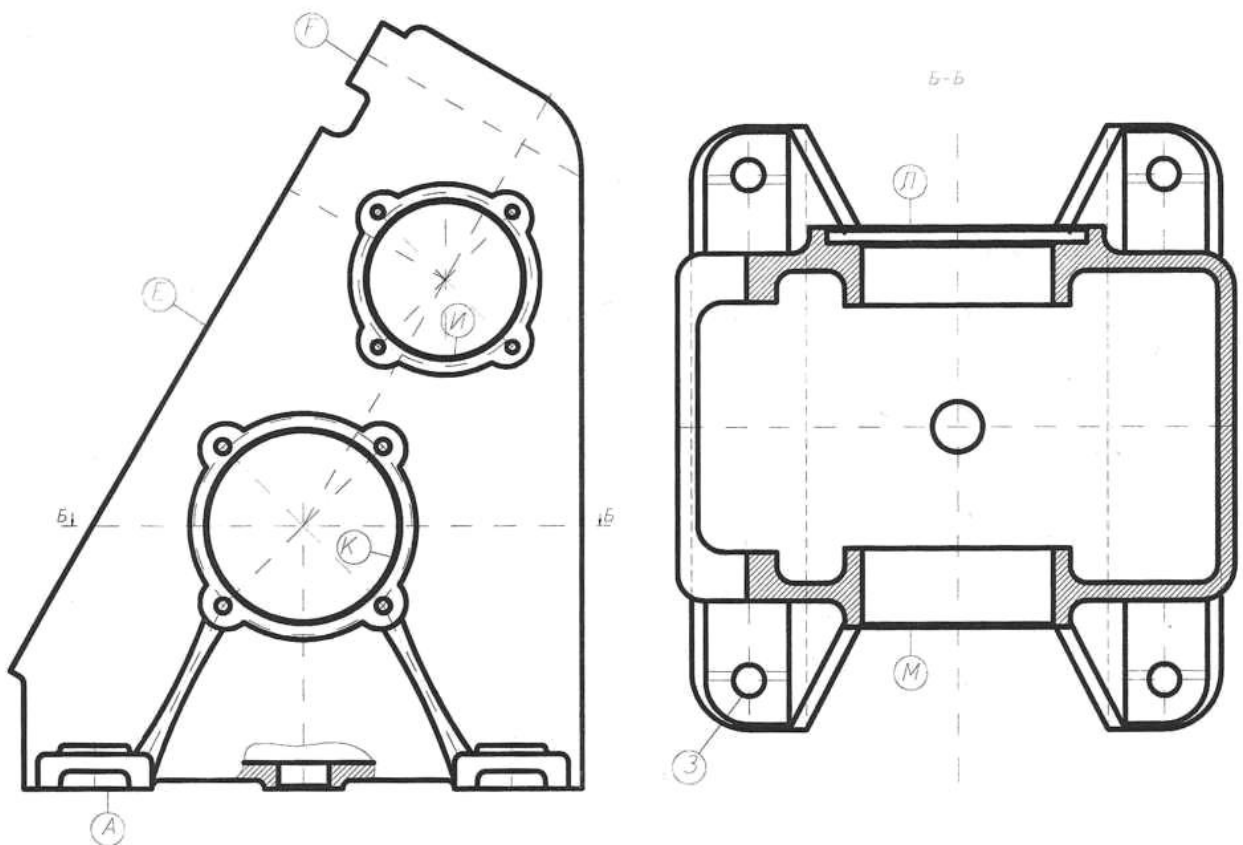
Позначення поверхонь деталі Корпус 47.7411.1158
